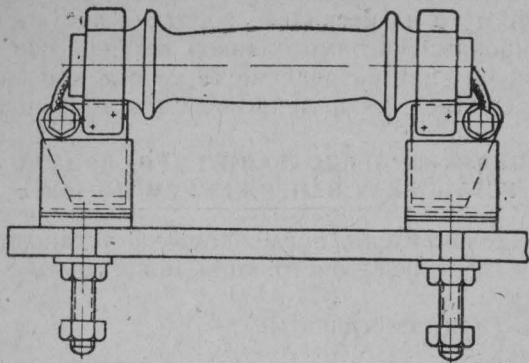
Трубчатый предохранитель с открытой фарфоровой трубкой типа СПО
